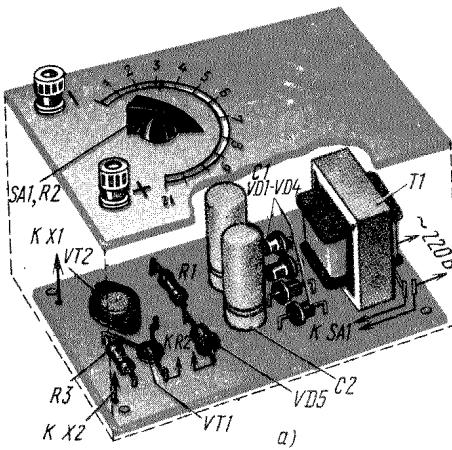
Конструкция сетевого блока питания и схема соединения деталей на монтажной плате
